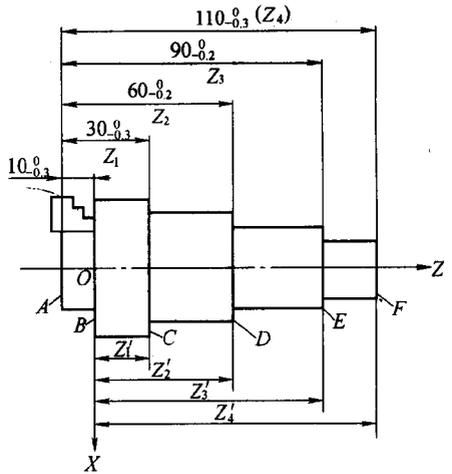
修改设计尺寸后的零图及轴向工序尺寸
